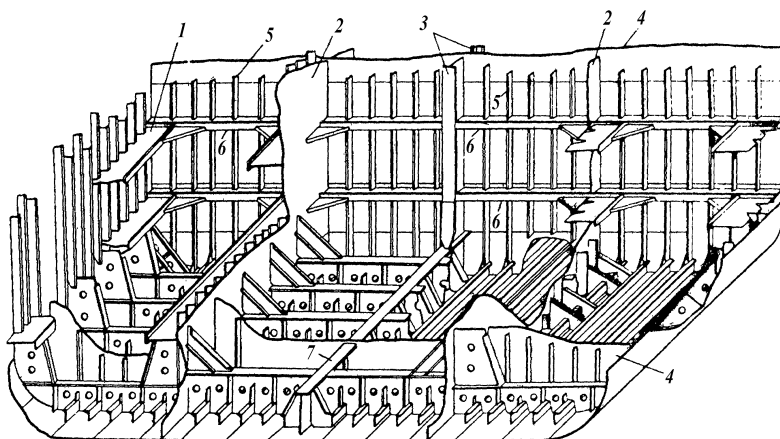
Конструкция плоских переборок: 1 – бортовой стрингер, 2 – продольная переборка, 3 – доковая стойка в ДП, 4 – поперечная переборка, 5 – стойка переборки, 6 – шельф, 7 – вертикальный киль
